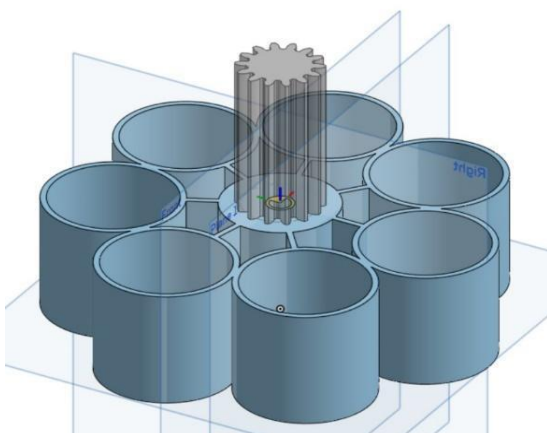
Приклад розташування шестерні, за допомогою інструмента Spur gear
